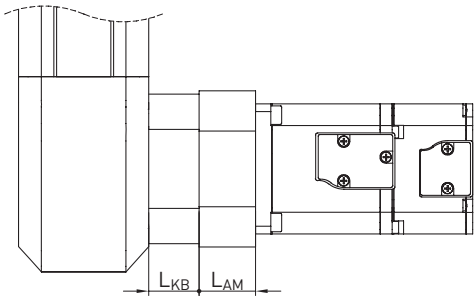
Motoranbindung Linearmodul HM-B ohne Getriebe
